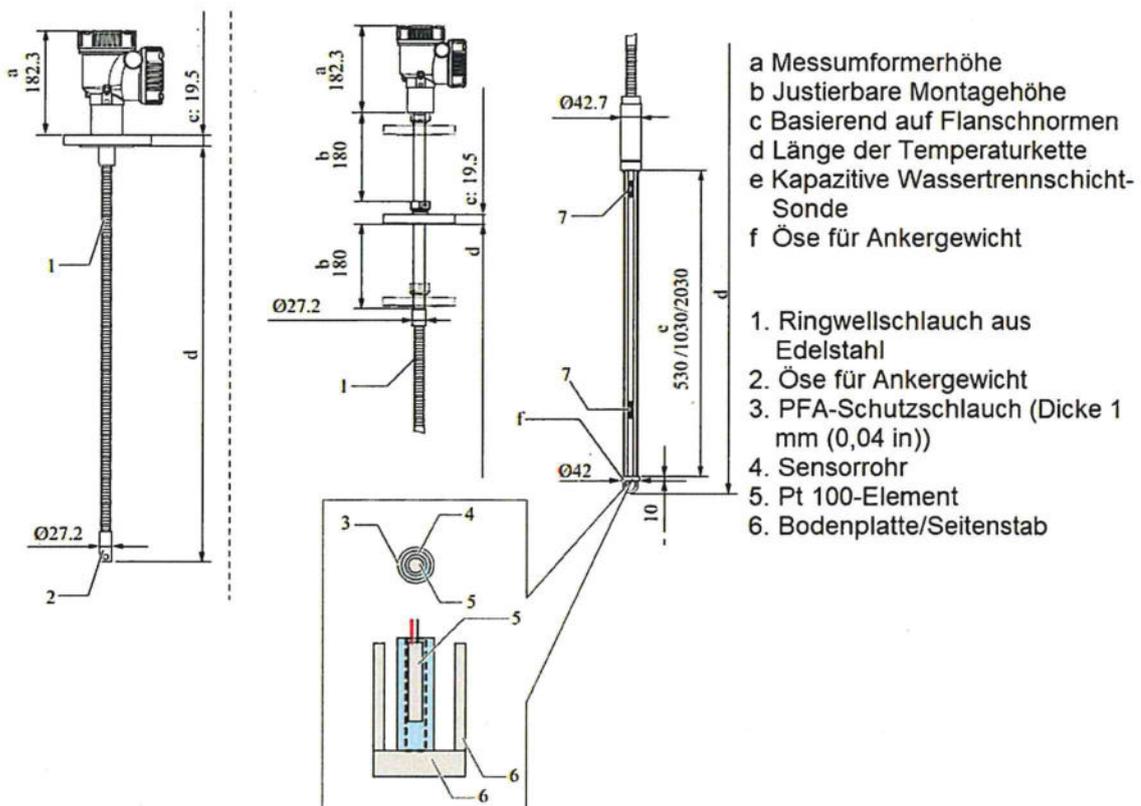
Prothermo NMT81 in den Ausführungen (von links): mit verschweißtem Flansch, mit einstellbarem Flansch, mit Wasserschichtmessung.
